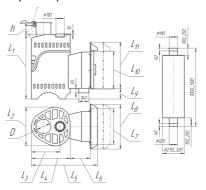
Общий вид печи, с нанесенными основными размерами.
